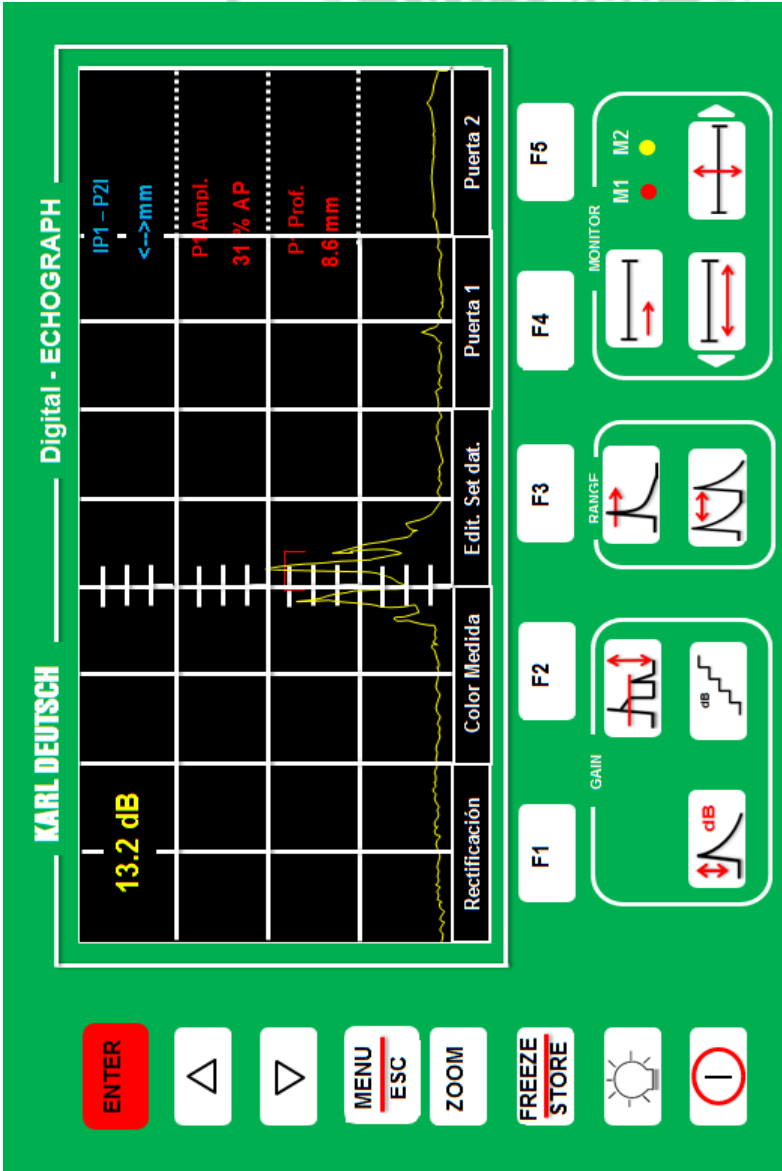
Pantalla de Inspección 2 lado izquierdo
